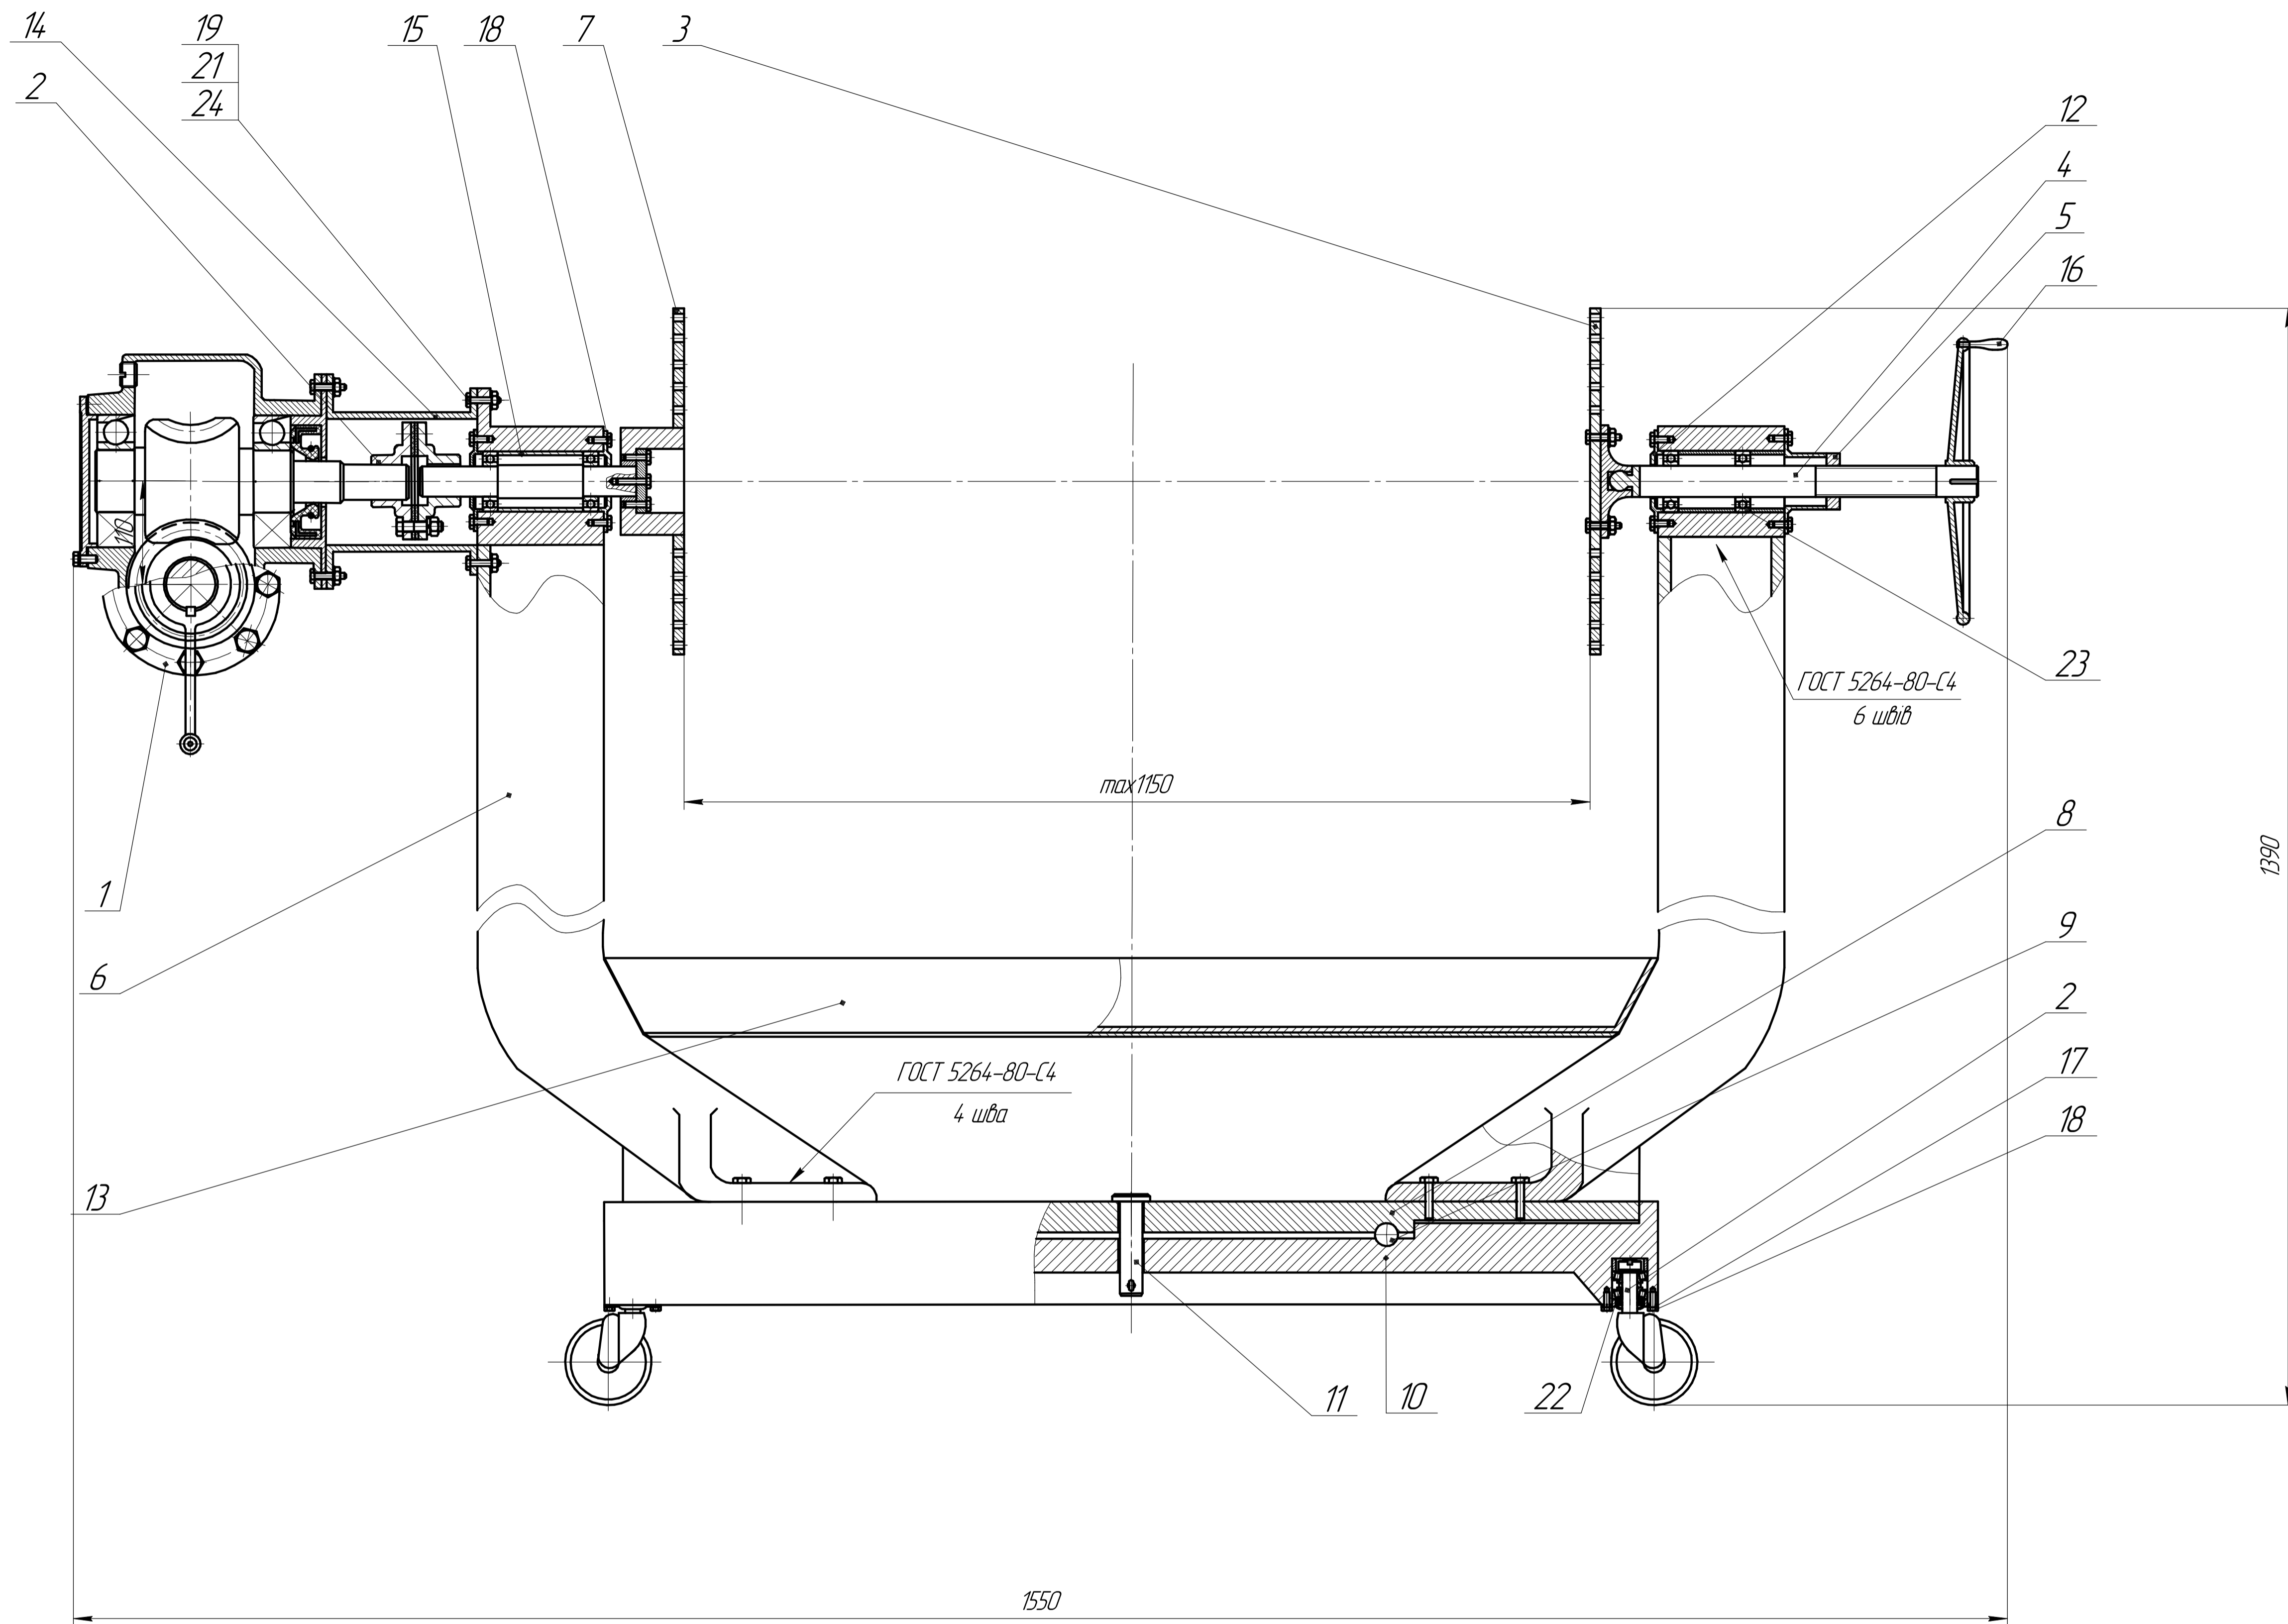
Зовнішній вигляд стенду для ремонту двигунів та коробок передач моделі B1337
